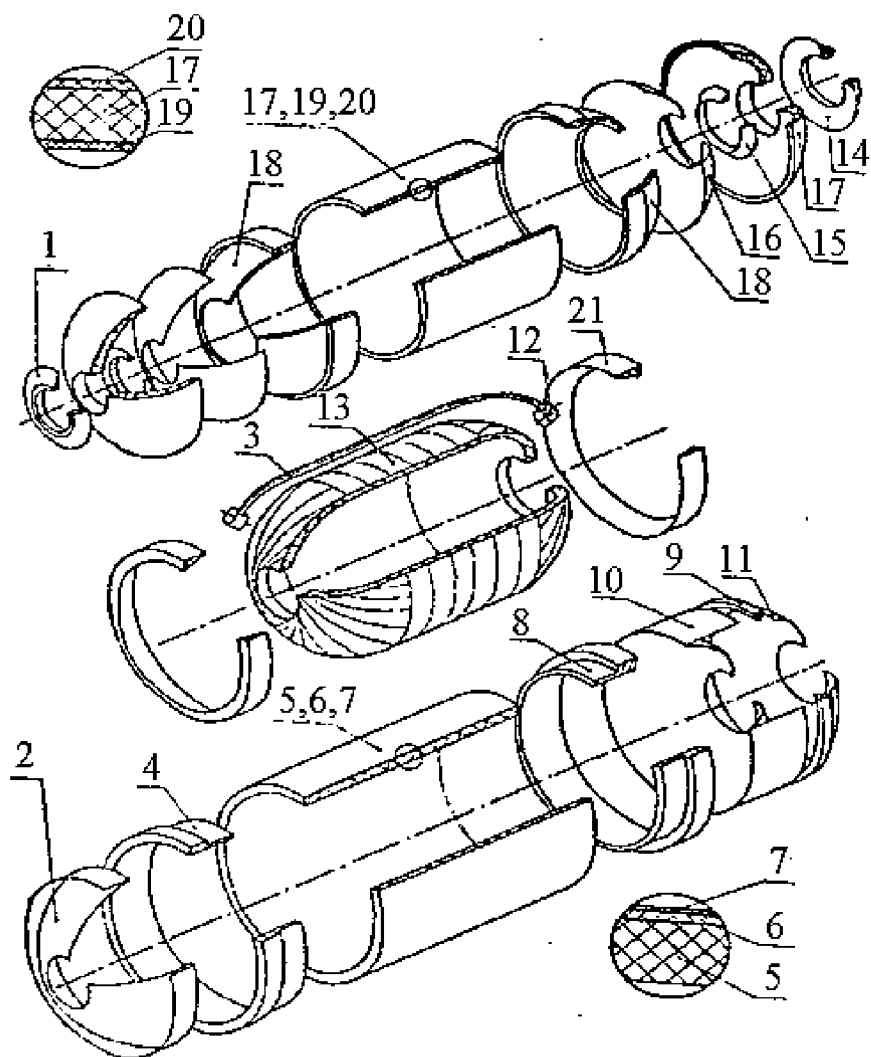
Элементы конструкции корпуса двигателя [2]: 1 - передний фланец; 2 - наружный герметизирующий слой переднего днища; 3 - бортовая кабельная сеть; 4 - передний шпангоут; 5 - второй кокон, 6 - слой для защиты от влаги и других внешних воздействий; 7 - лакокрасочное покрытие; 8 - задний шпангоут; 9 - ДУЗ; 10 - наружный герметизирующий слой заднего днища; 11 - наружный покрытие из ТЗМ, 12 - разъем бортовой кабельной сети; 13 - силовая оболочка (первый кокон); 14 - задний (сопловой) фланец; 15 - клин, 16 - анти адгезионная пленка; 17 - внутреннее покрытие из ТЗМ; 18 - манжеты; 19 - ЗКС; 20 - герметизирующий слой; 21 - эластичный клин
